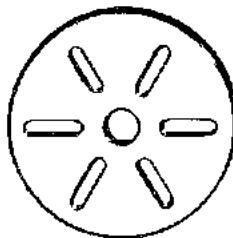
Plato frontal (Sheldon Machine Co., Inc.)
